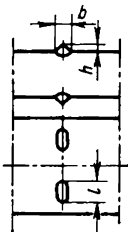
Двусторонняя метка для контроля величины несовпадения ручья
